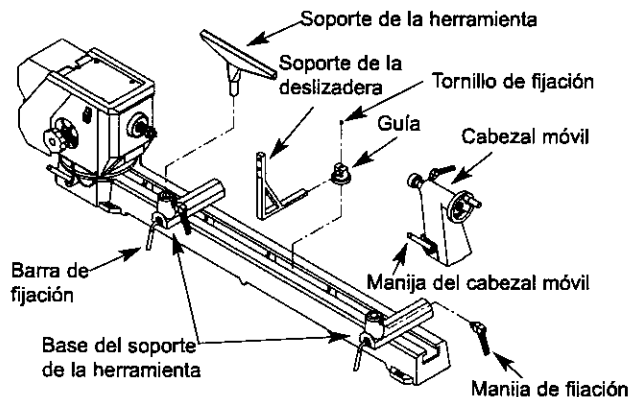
Acople la Base del Soporte de la Herramienta a la Base del Torno (Modelo 24951)
